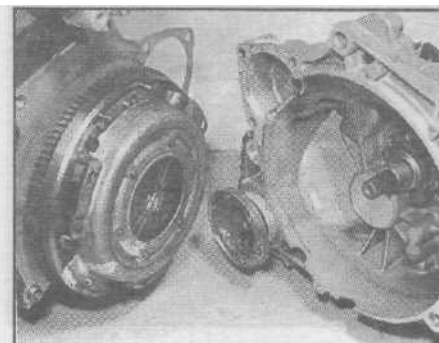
, б. ... затем разделите двигатель и коробку передач
